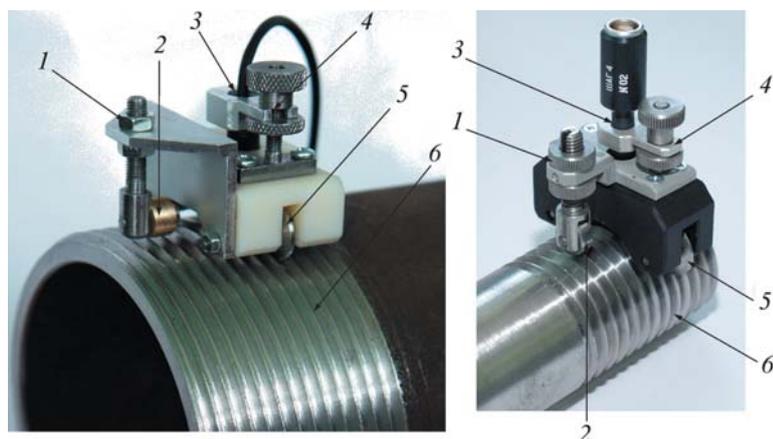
Сканирующие устройства для контроля наружной конической резьбы буровых труб:
